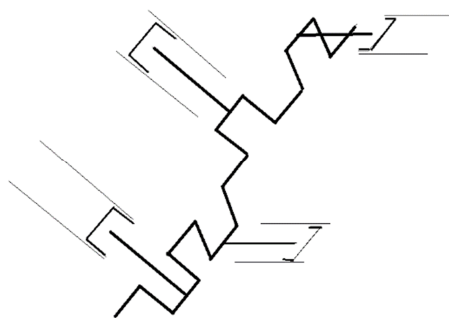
Схема V-образного четырехцилиндрового двигателя
